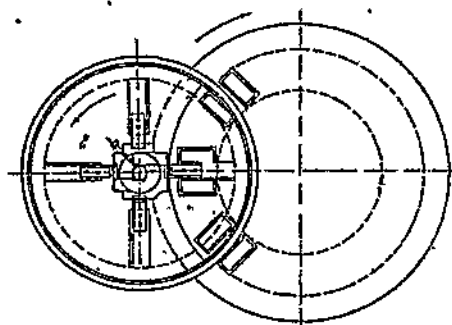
Поворотный стол пресса с гнездами и шаталом с ножами:
